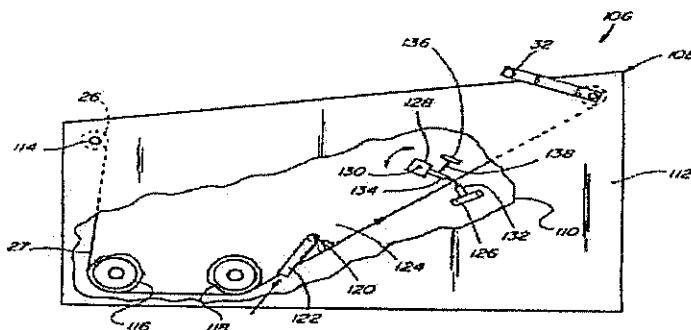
ภาพ Partial Section จากมุมมองด้านหน้าของเครื่อง Plastic Sheet Cleaning Machine
